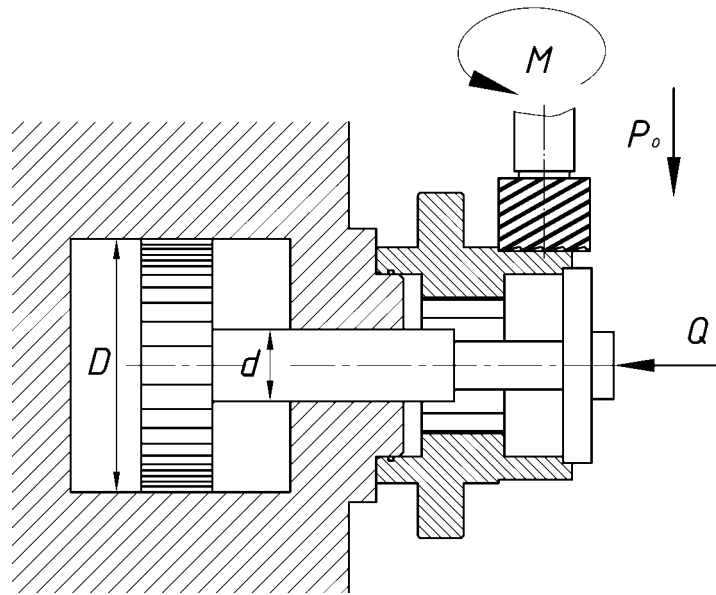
Схема базування та затиску заготовки у пристрої для фрезерування площин
